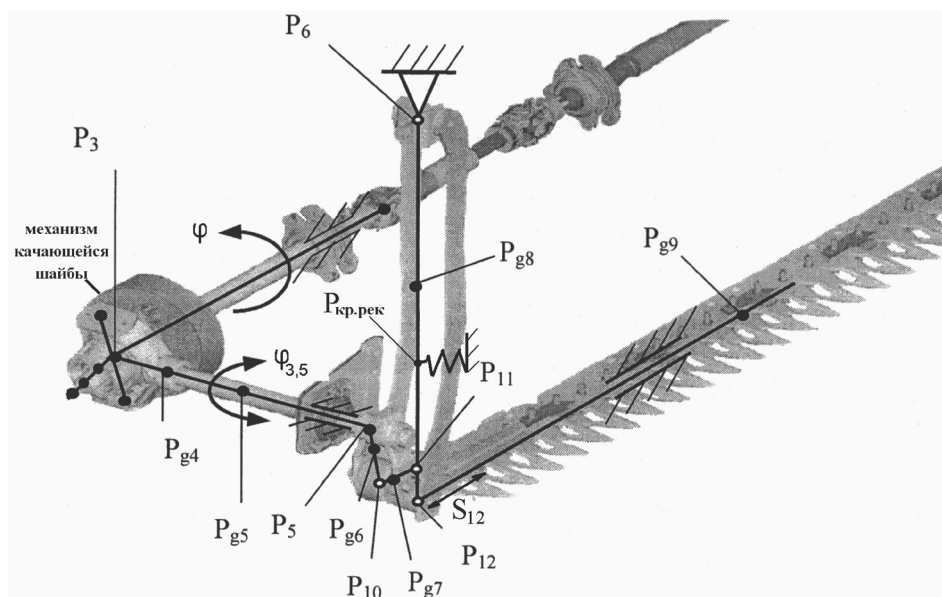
Кинематическая схема привода ножа режущего аппарата жатки
